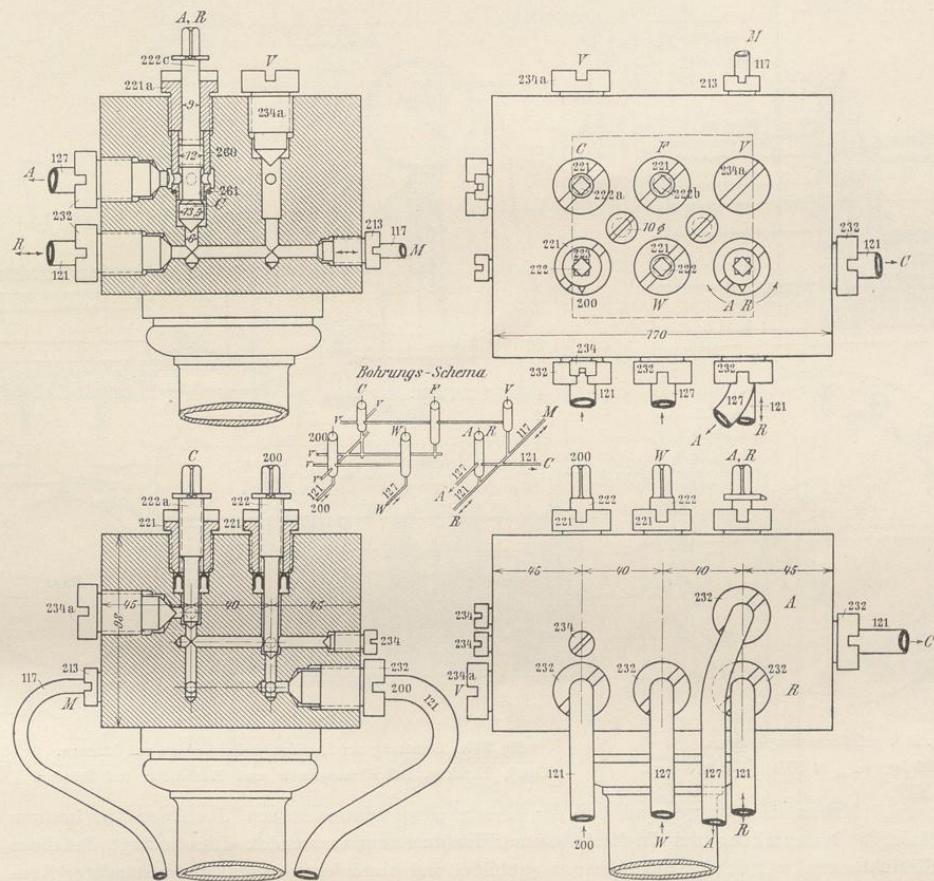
Steuerung der Werder- und Martens-Maschinen.
